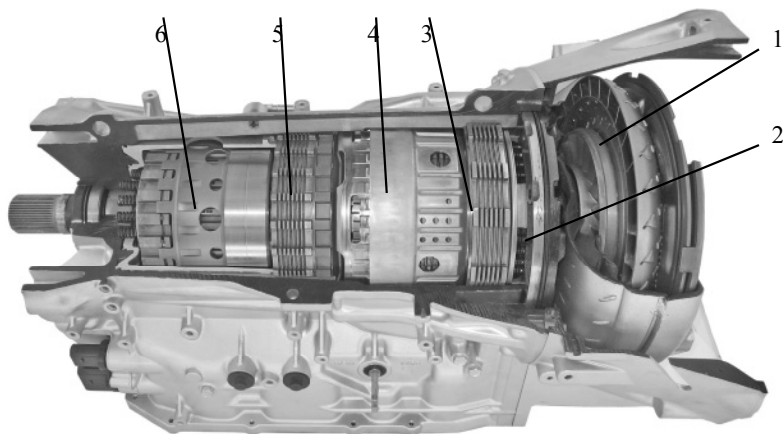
Гидромеханическая коробка передач Aisin:
